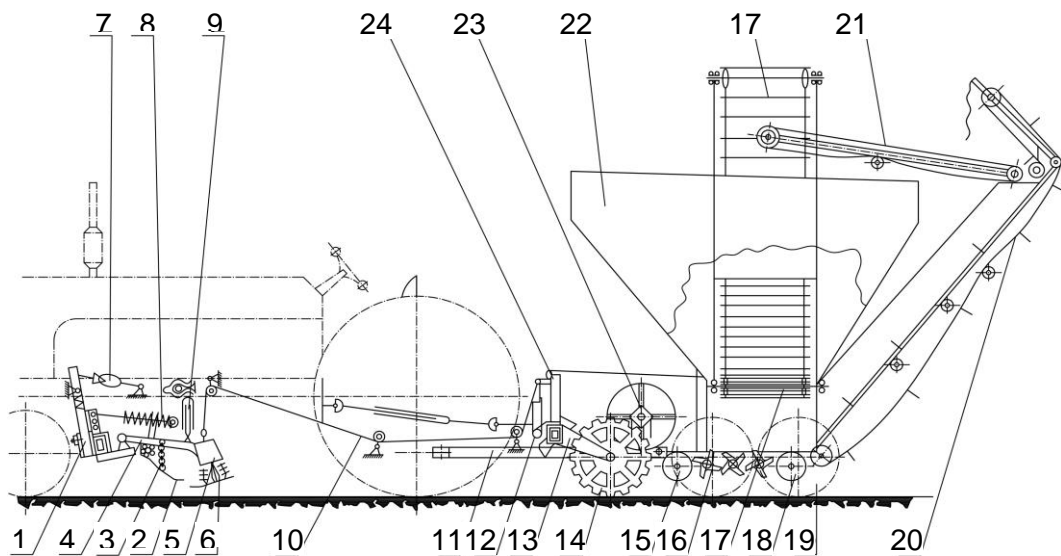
Конструктивна схема збирального комбайна фірми «Фармхенд-350»: 1 – автомат керування; 2 – копір; 3 – пружина; 4 – тяга; 5, 6 – кожух і гичкозрізувальний диск; 7 – механізм регулювання щупа; 8 – пружина копіра; 9 – гідроциліндр; 10 – механізм регулювання дискового ножа зрізування гички; 11 – сниця; 12 – тяга; 13, 14 – копач; 15, 18 – вал; 16 – очисник вороху; 17, 20, 21 – транспортери; 19 – опорне колесо; 22 – бункер; 23 – бітер; 24 – рама
